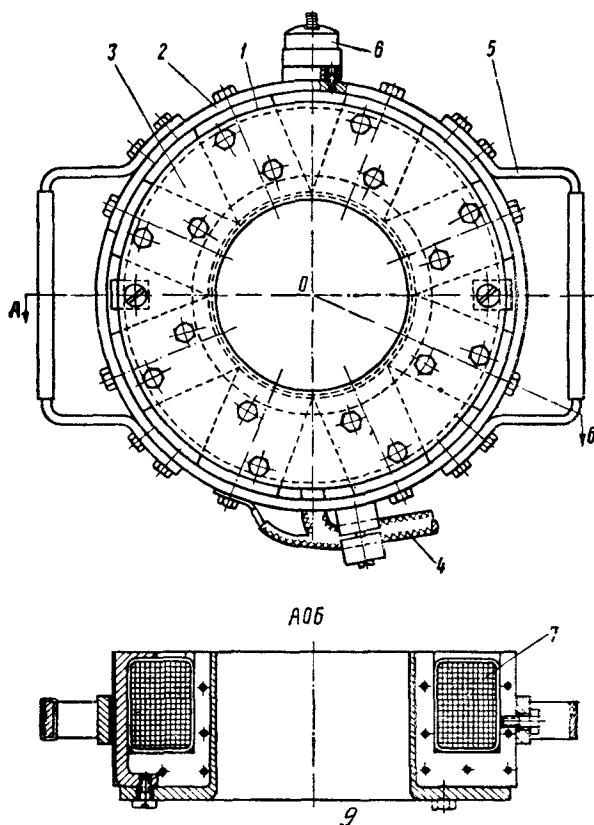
Индукционный нагреватель для снятия подшипниковых колец и лабиринтовых втулок с вала якоря:
